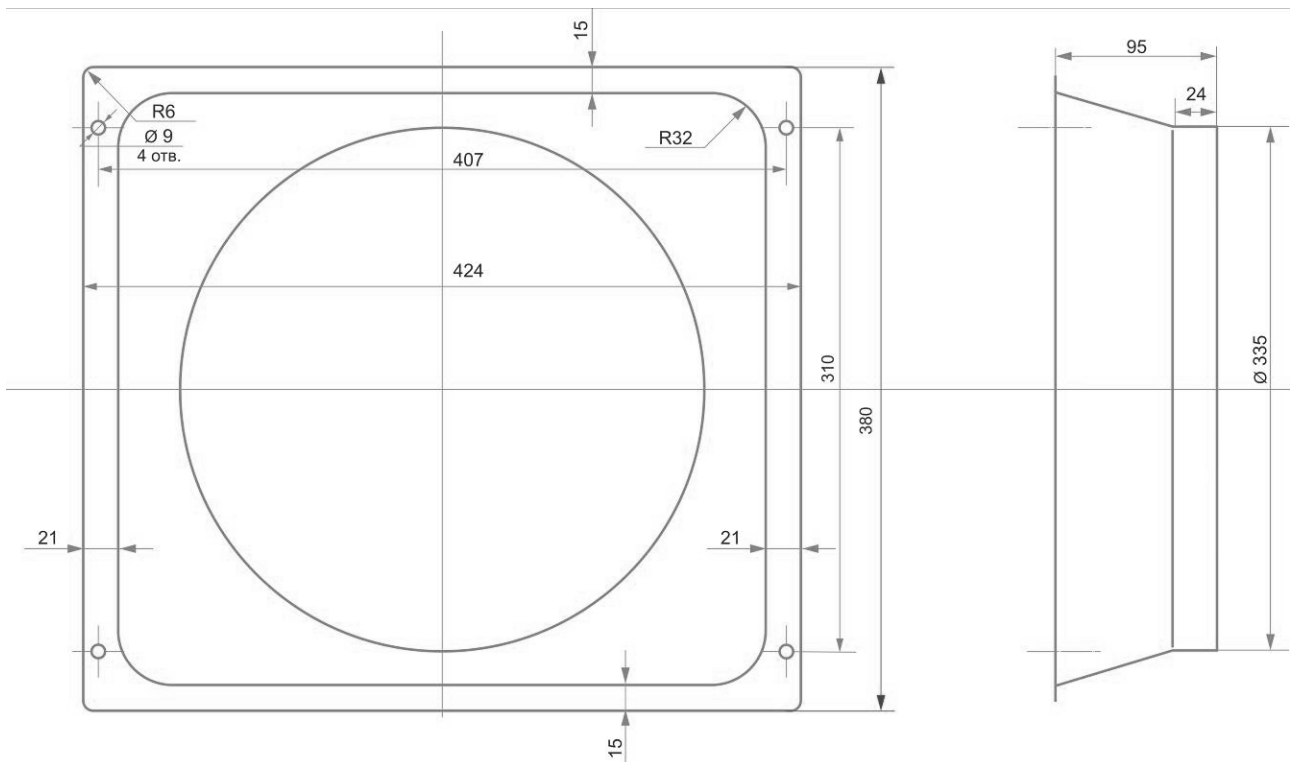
Робоче креслення кожухозабірного дефлектора.
